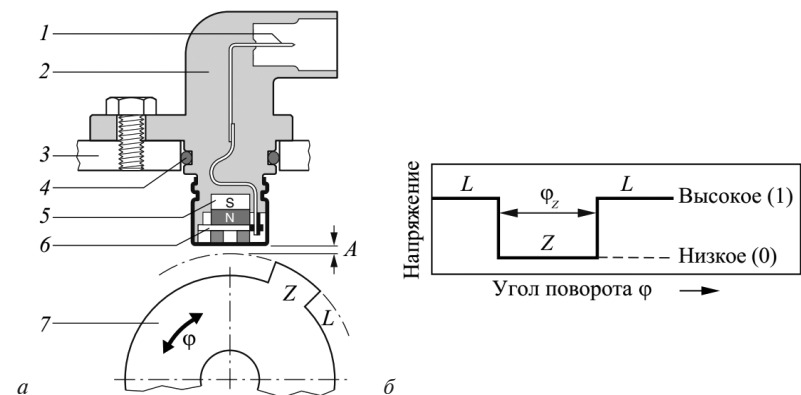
Датчик положения распределительного вала с элементом Холла: а – общее устройство; б – сигнал датчика; 1 – штекер; 2 – корпус датчика; 3 – корпус двигателя; 4 – уплотнительное кольцо; 5 – магнит; 6 – интегральная схема датчика Холла; 7 – колесо с зубчатым сегментом
